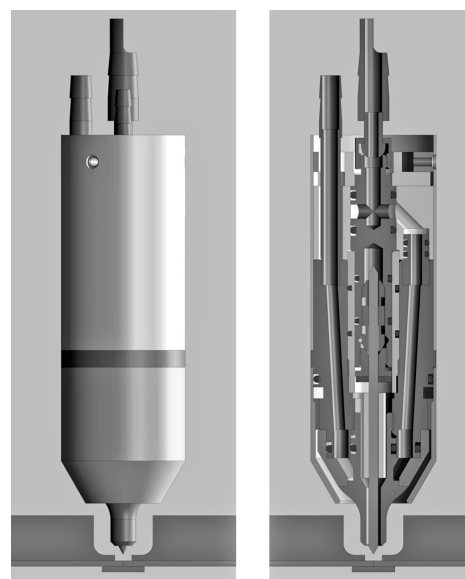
Плазматрон с соплом для «мягкой плазмы» для сварки в зазоре шириной до 14 мм и толщиной листов до 14 мм
